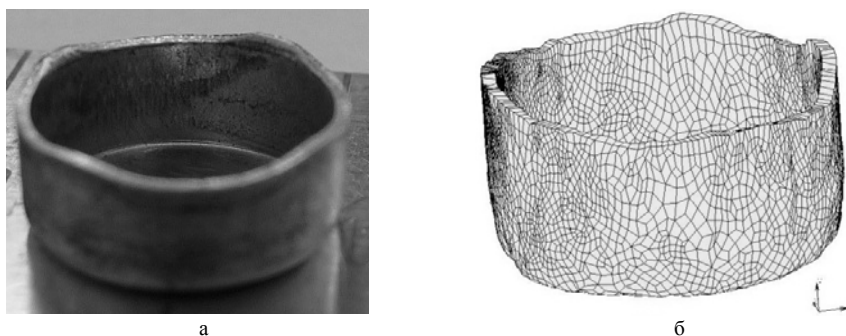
Общий вид полый цилиндрической детали: а – реальное изделие; б – КЭМ
